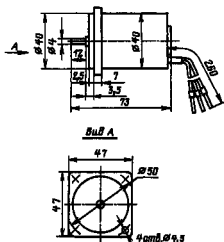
5 Габаритные и установочные размеры двигателя ДАТ21920
